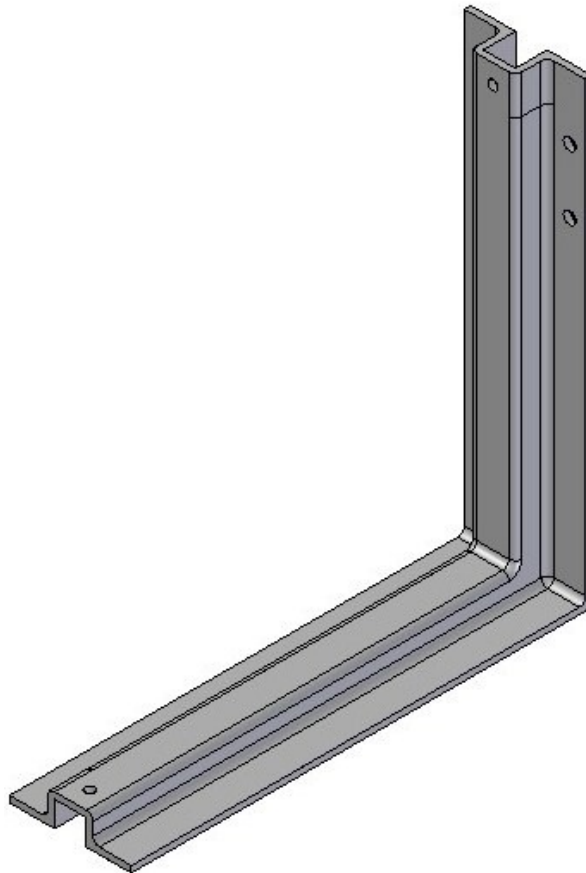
Fuerzas sobre el soporte del tanque de combustible
